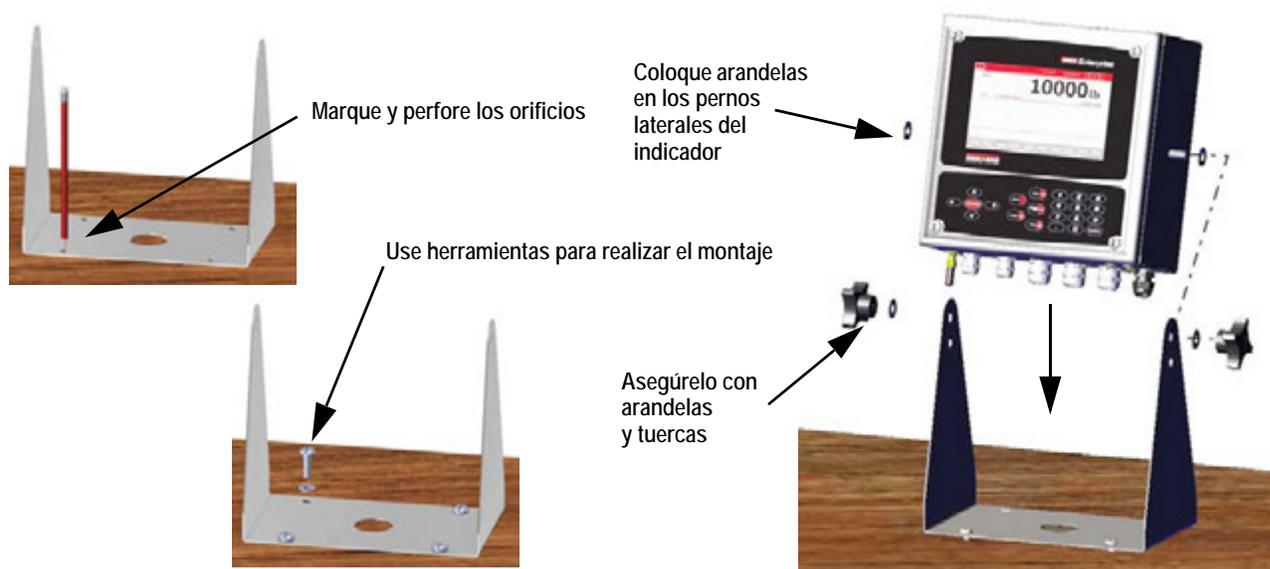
Montaje del indicador 1280 – Gabinete universal
